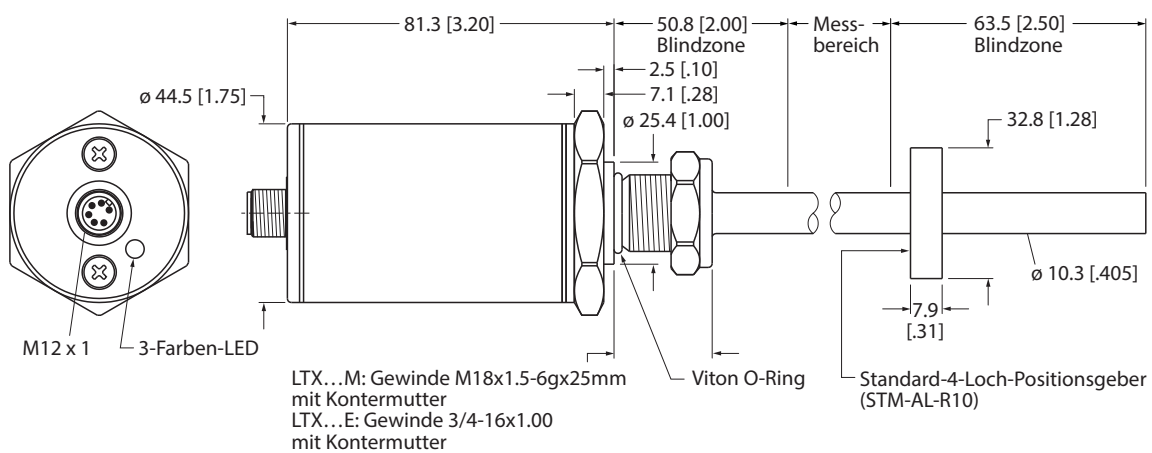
Seitenansicht LTX-R10 mit Abmessungen in mm [in] (Ausführung mit Raised Face)
